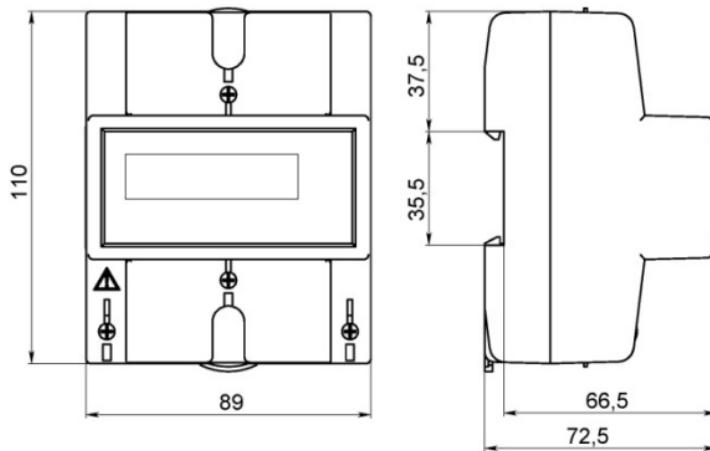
Габаритные и установочные размеры счетчика в корпусе R5
